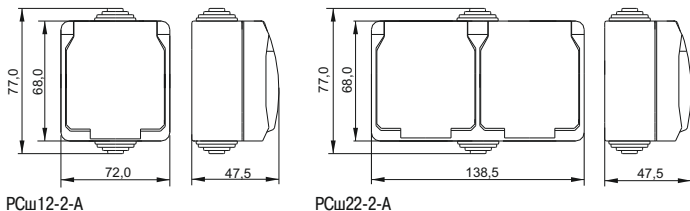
Габаритные и установочные размеры розеток / Figure 2 – Overall and installation dimensions of the sockets / 2 сурет – Розеткалардың габариттік және орнату өлшемдері / Imaginea 2 – Dimensiuni și dimensiuni de instalare a prizelor
